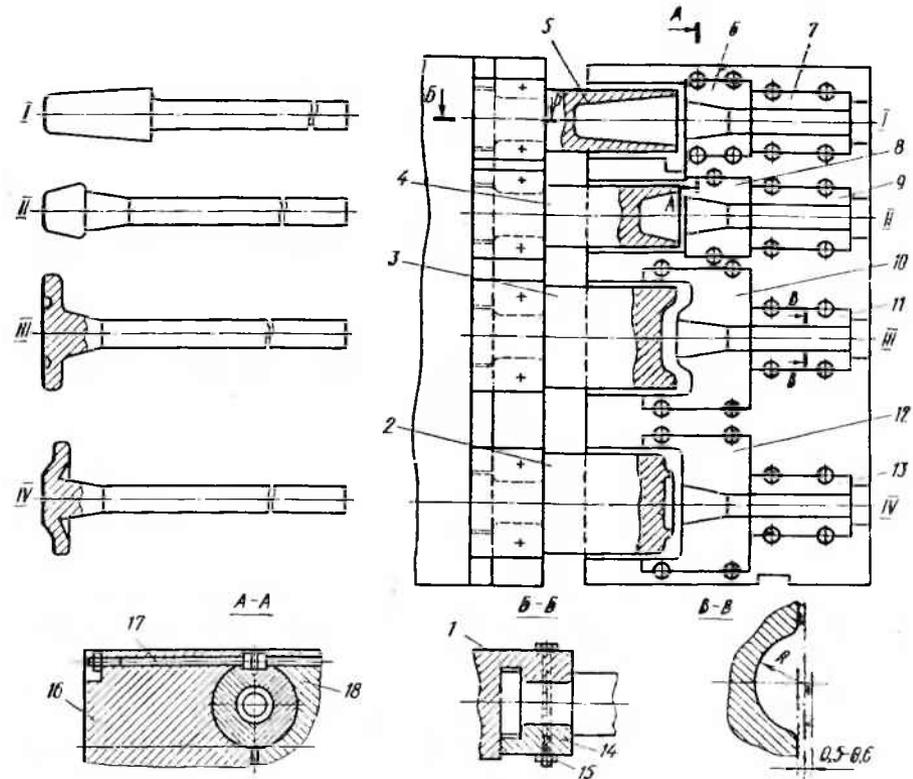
Четырехручьевого штампа для высадки поковки полуоси автомобиля
